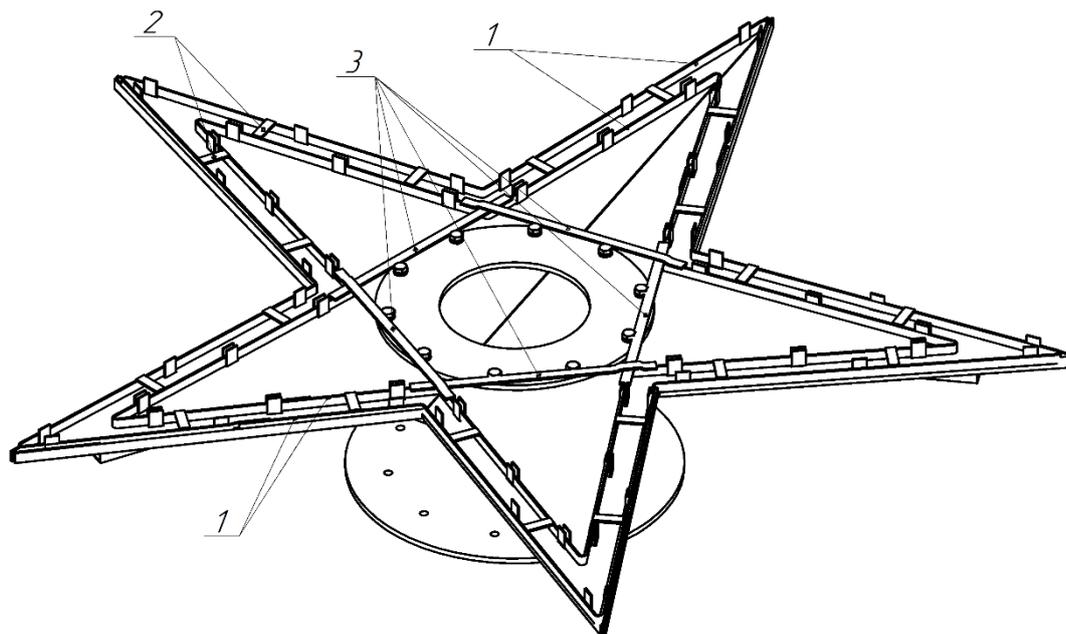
Процесс сборки сварного каркаса
